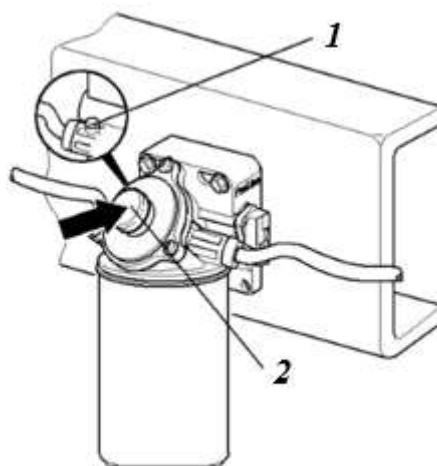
Удаление воздуха из корпуса топливного фильтра
